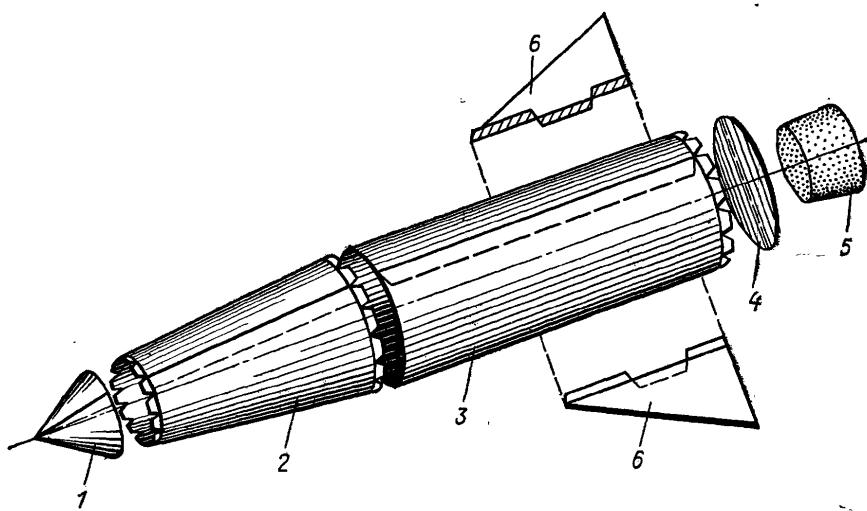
Порядок изготовления элементов и сборки модели (показаны только два стабилизатора).
